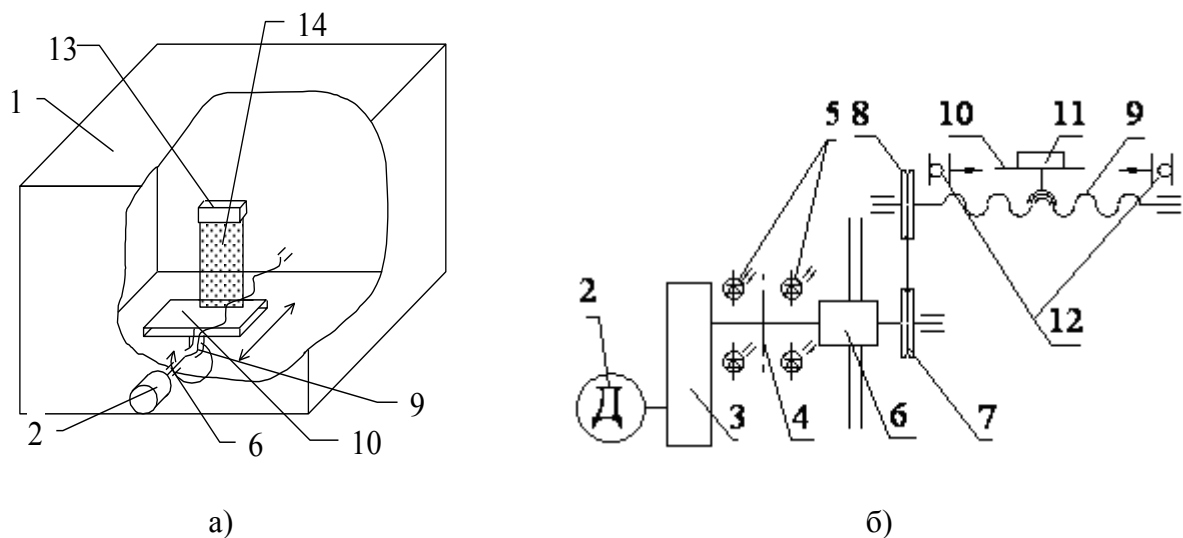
Конструкція (а) і кінематична схема (б) механізму переміщення оптичних виробів при їх обробці електронним потоком: 1 – вакуумна камера; 2 – електропривід; 3 – редуктор; 4 – перфорований диск; 5 – оптопари; 6 – вакуумний увід; 7 – шків; 8 – колесо; 9 – ходовий гвинт; 10 – основа із затискним пристроєм; 11 – оптичний виріб; 12 – кінцеві датчики; 13 – модуль електронно-променевої гармати Пірса; 14 – стрічковий електронний потік
